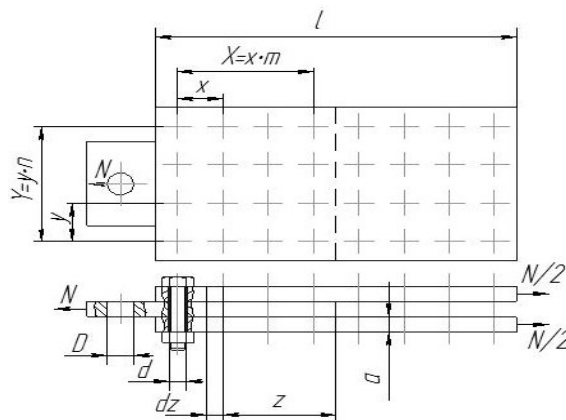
Схема нагружения болтовых соединений с зазором сдвигающими силами
